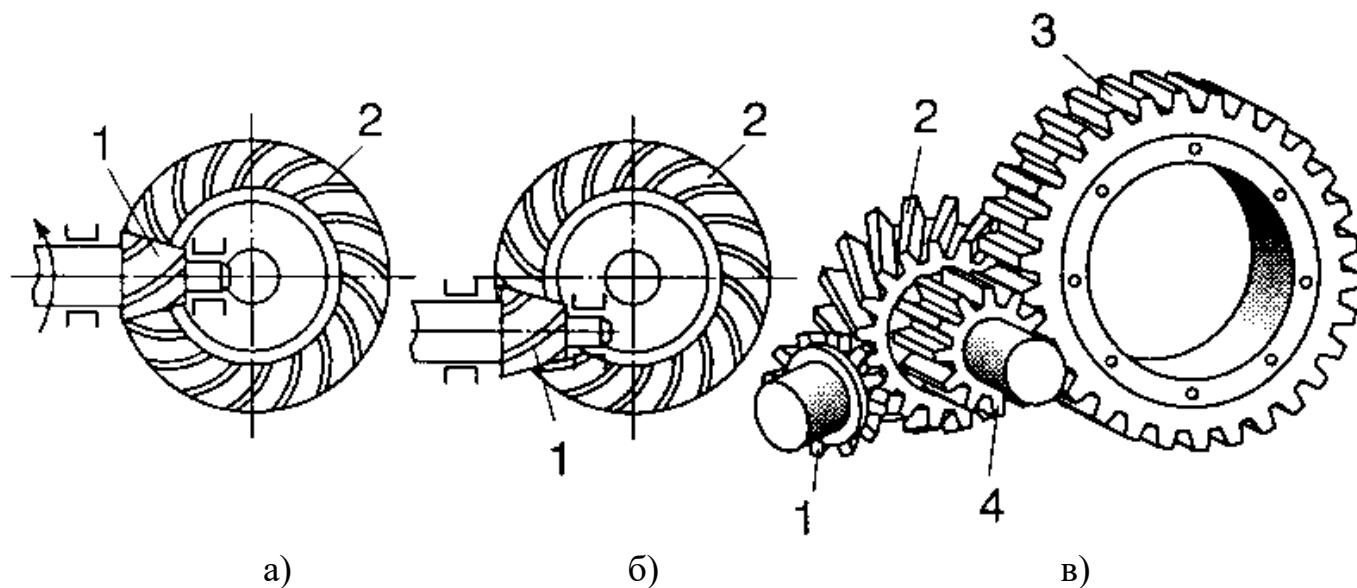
Головна передача: а - одинарна із спіральними шестернями; б - одинарна гіпоїдна; в - подвійна: 1 - ведуча конічна шестерня; 2 - ведена конічна шестерня; 3 - ведена циліндрична шестерня; 4 - ведуча циліндрична шестерня.
